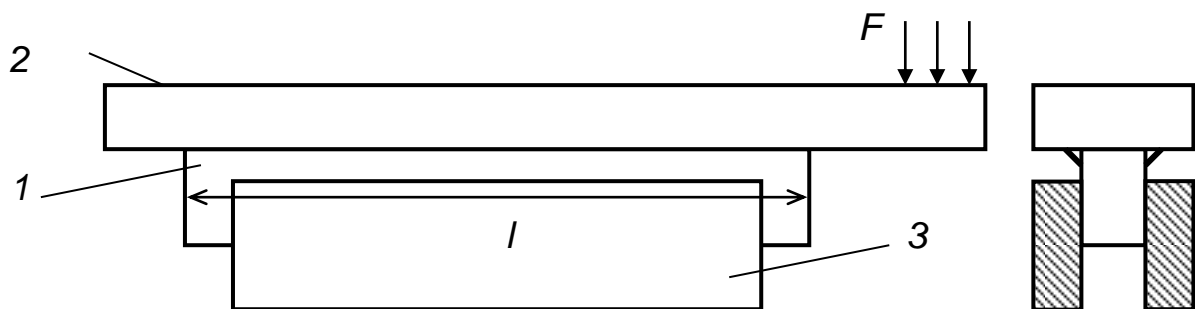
Схема з'єднання кріпильної пластини із корпусом:
